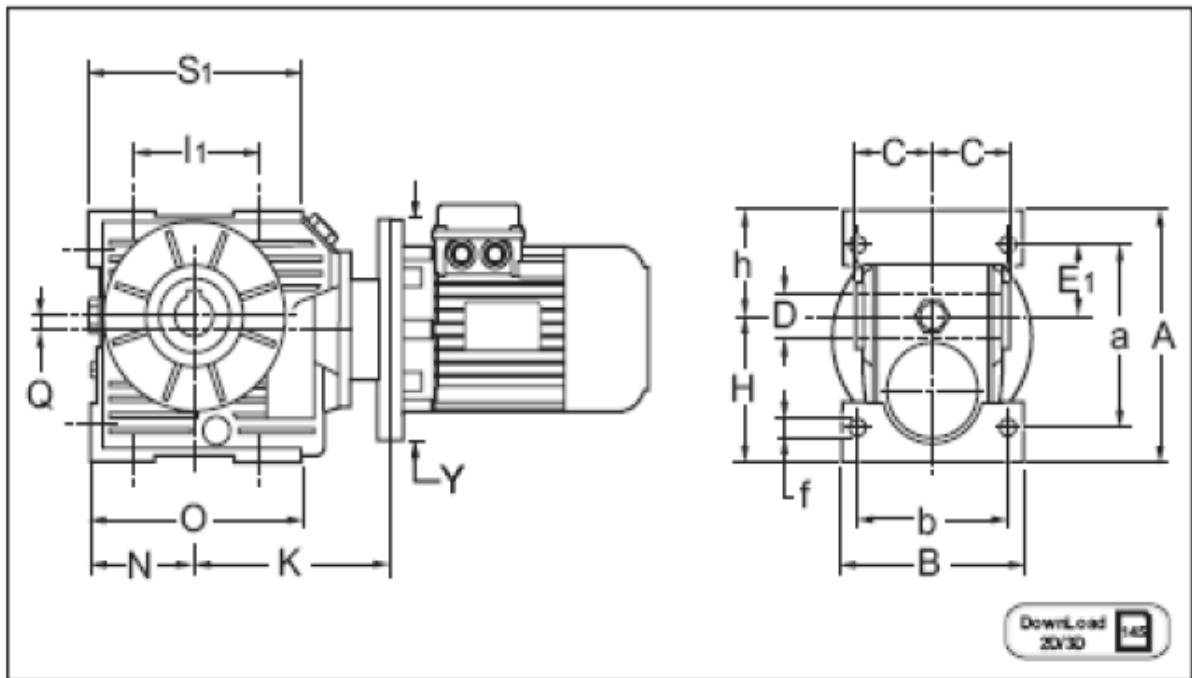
Ескіз мотор-редуктора СВ 70.
